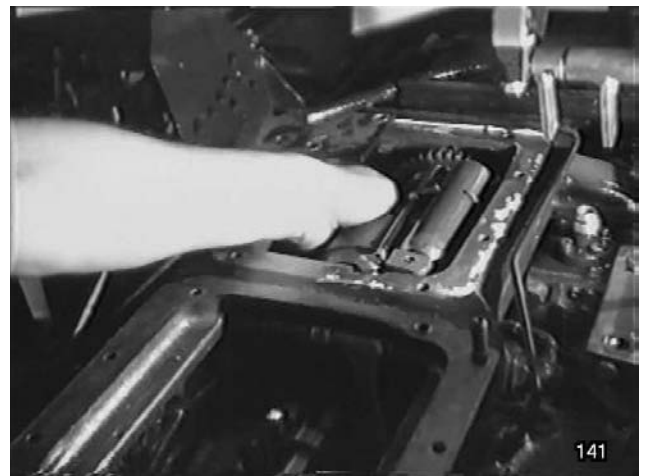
Déposer le relevage et le couvercle avant du carter de boîte arrière et accéder à l'ensemble de l'embrayage de la P.d.F.
